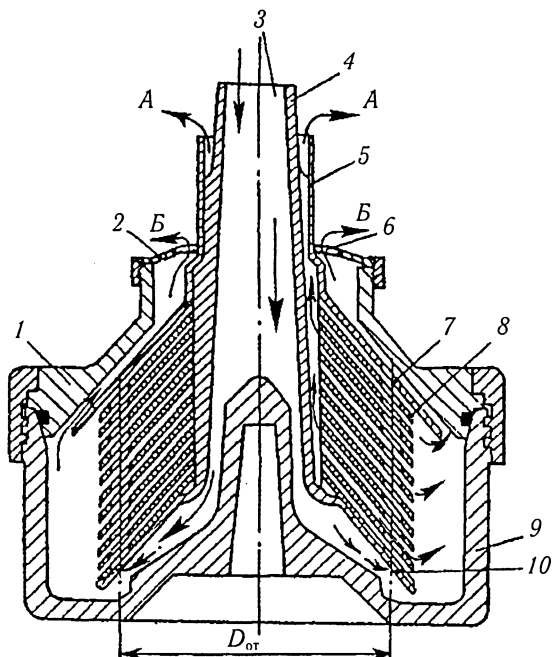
Схема барабана — пурификатора: 1 — крышка барабана; 2 — регулировочная шайба; 3 — центральный канал; 4 — тарелкодержатель; 5 — патрубок для выхода топлива; 6 — отверстие в регулировочной шайбе; 7 — разделительная тарелка; 8 — тарелки сепаратора; 9 — барабан; 10 — отверстия в нижней тарелке
